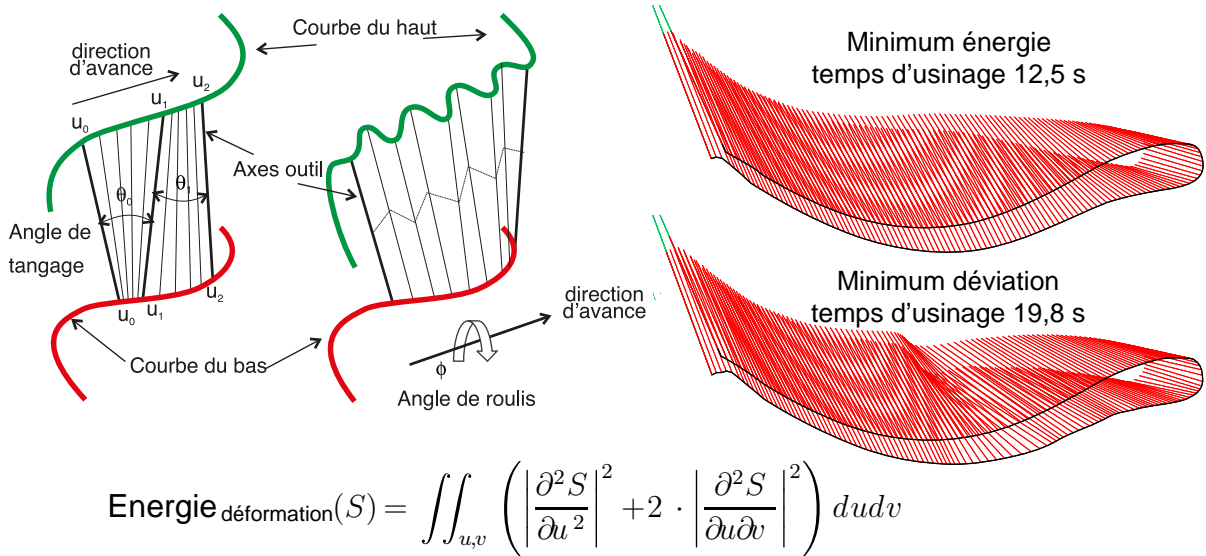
Intégration d’un critère de fluidité pour l’usinage sur le flanc [Péchar, 2009]
